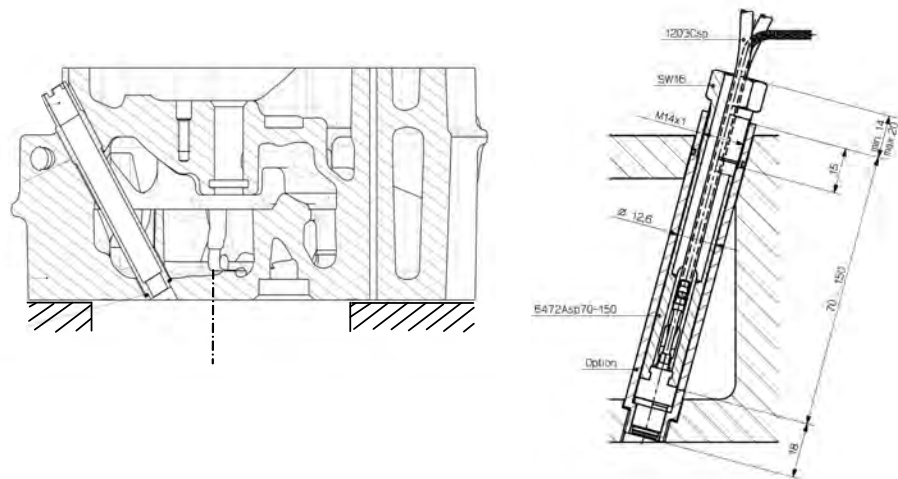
Zylinderkopf und Piezo-Drucksensor zur Druckindizierung im Brennraum
